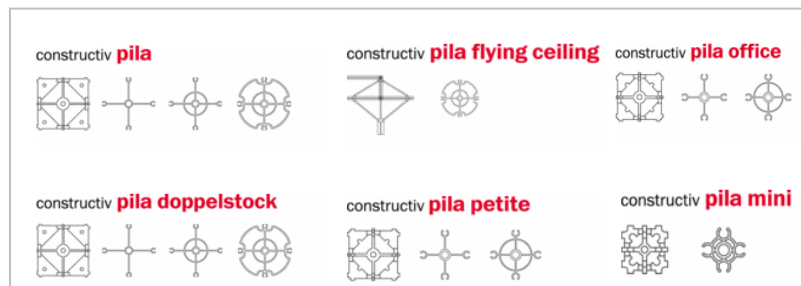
Família PILA, cortes transversais dos elementos de conexão. Fonte: LEITNER, 2011.
